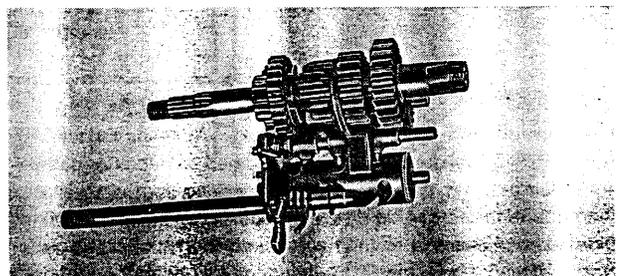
Engrenages avec manœuvre de changement de vitesses (vue de dessous)
